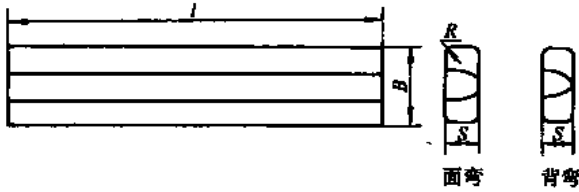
焊接接头纵向面弯和背弯试样形状和尺寸
